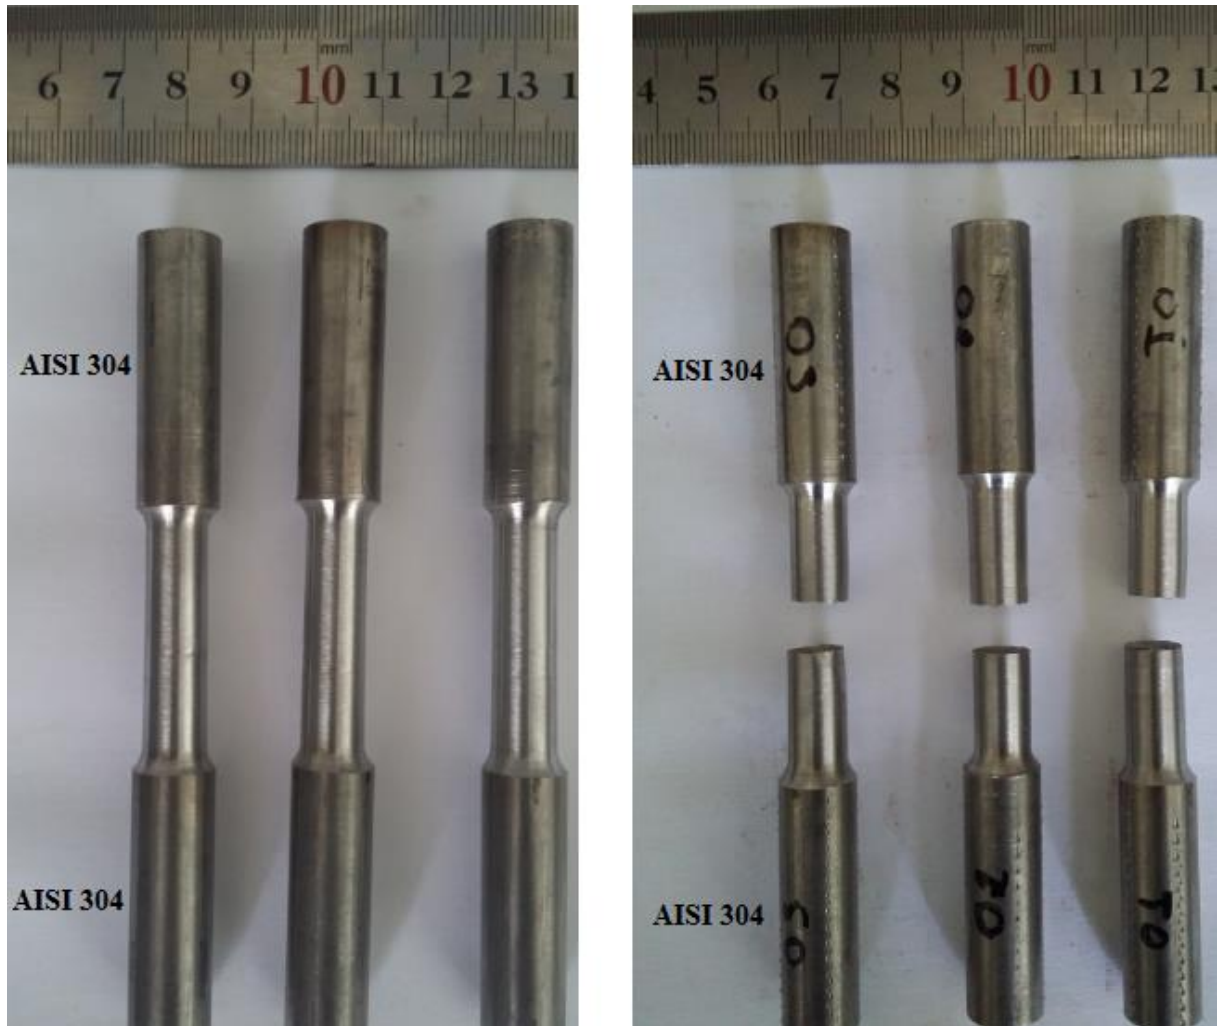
Corpo de prova 23; 3-2-2. Soldagem similar do aço AISI 304 e ensaio de tração
